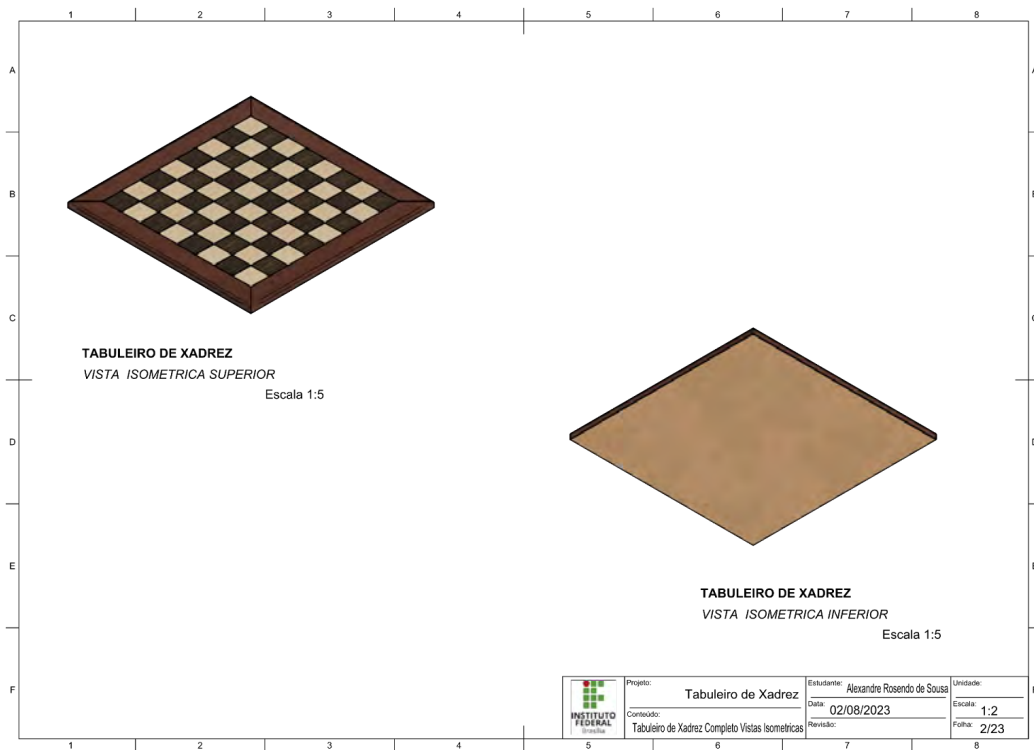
Tabuleiro de Xadrez Desenho Técnico Vistas Isométricas
